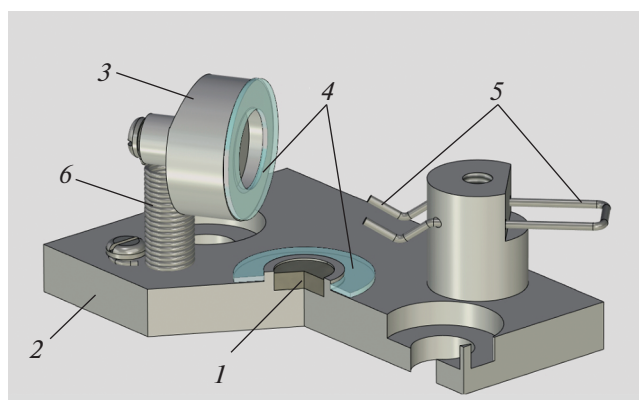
Схема транспортного контейнера. 1 — образец; 2 — пластина; 3 — колпачок; 4 — вакуумная замазка; 5, 6 — пружины.
